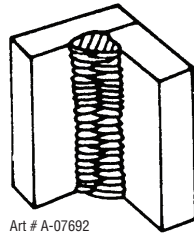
Posición vertical, soldadura de ángulo
